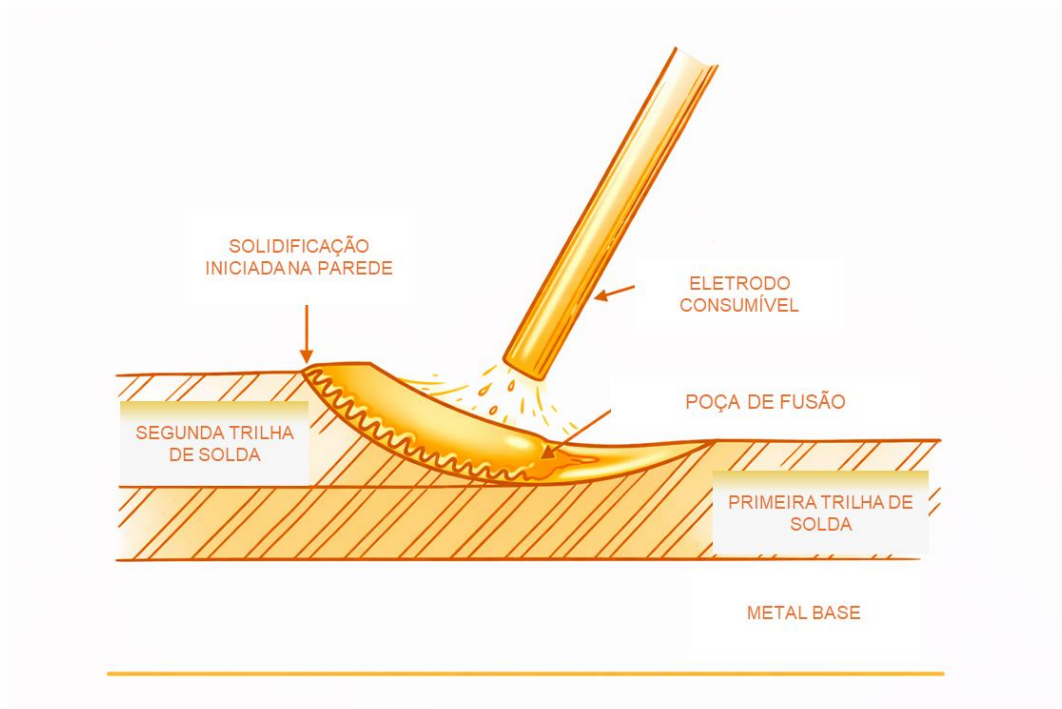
Figura esquemática de soldagem utilizando eletrodo revestido, formando mais de uma camada. Adaptado de *Welding metallurgy*, Linnert, vol. 2, ch. 13 p. 189-306. [47].
